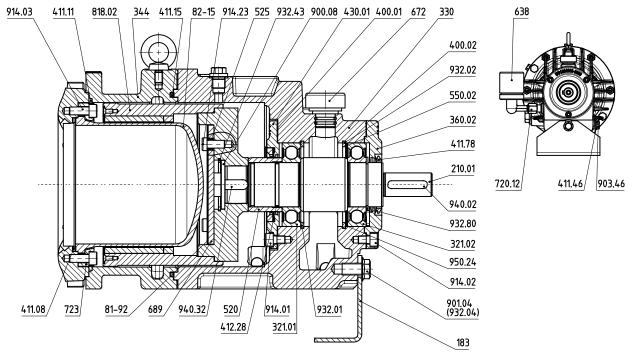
Исполнение подшипникового кронштейна с жидкой смазкой и уплотнительным кольцом вала в качестве защиты от утечек
